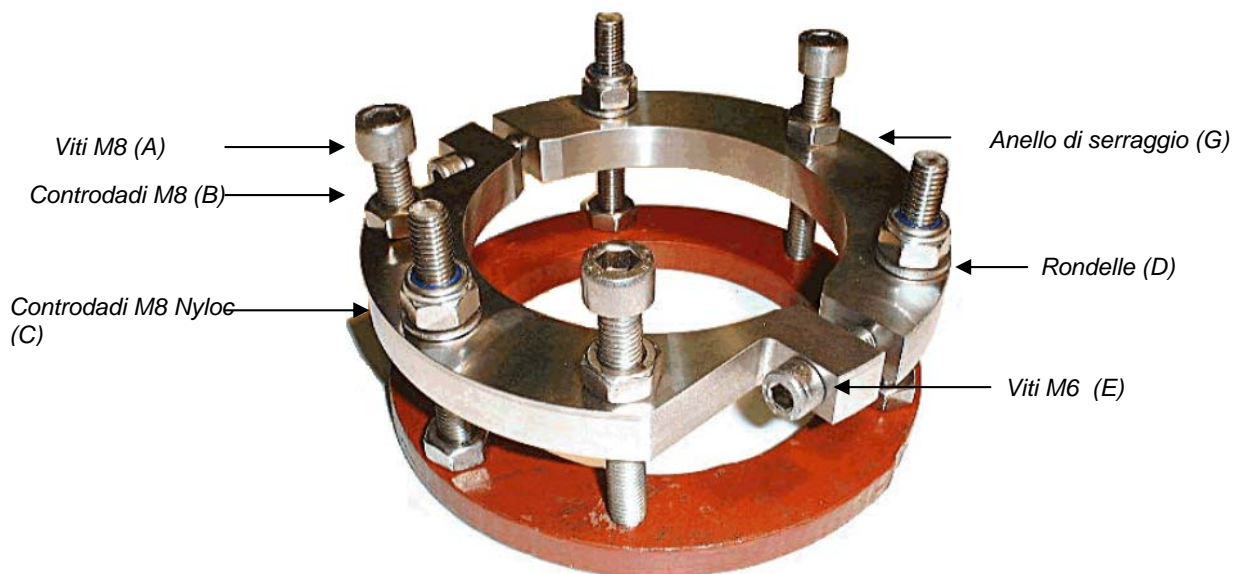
Anello di serraggio assemblato e montato sulla piastra di fissaggio
